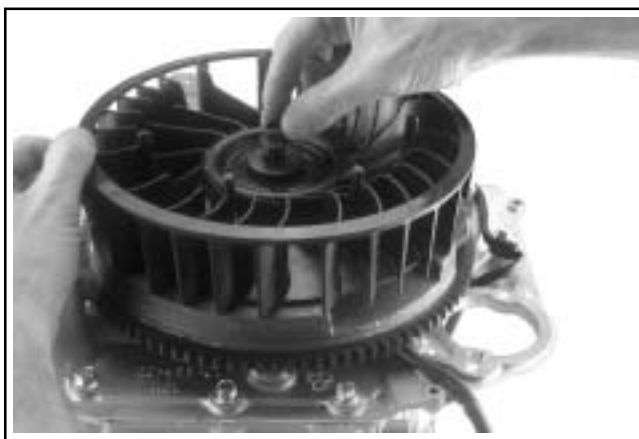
Instalación del ventilador y los accesorios de montaje en el volante.
